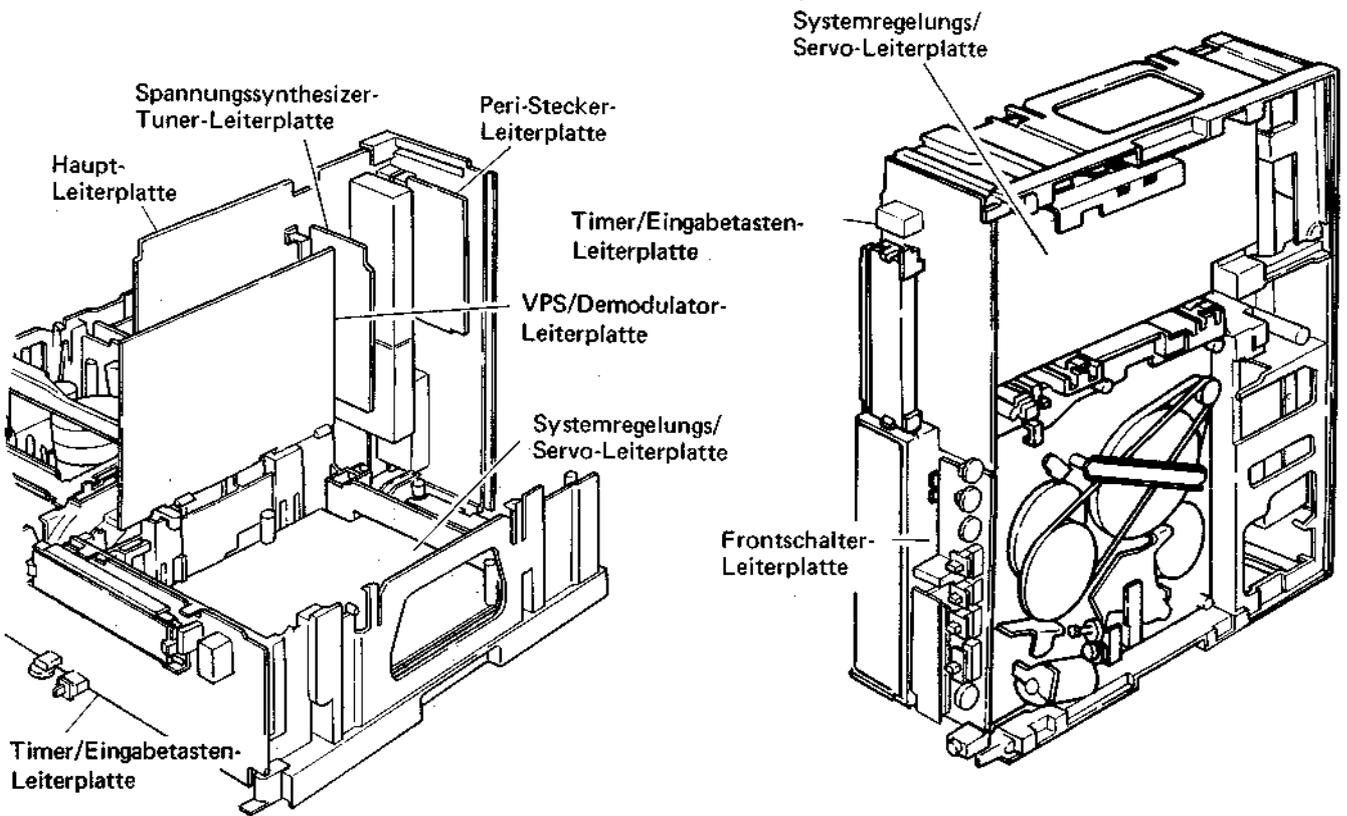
Draufsicht (mit geöffneter Haupt-Leiterplatte)
